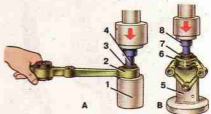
Выпрессовка резинометаллических шарниров из рычага подвески и кронштейна крепления растяжки: 1 – втулка; 2 – рычаг подвески; 3 – резинометаллический шарнир; 4 – оправка; 5 – приспособление 67.7823.9540; 6 – кронштейн крепления растяжки; 7 – резинометаллический шарнир; 8 – оправка
